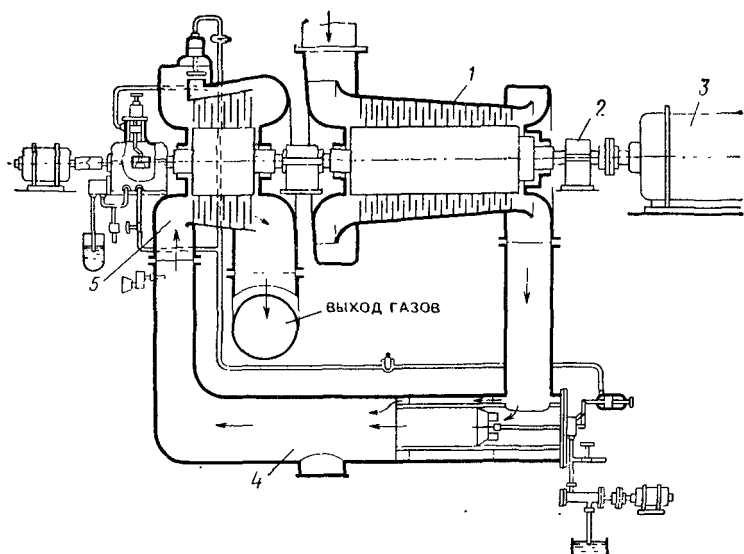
Схема установки осевого компрессора с газовой турбиной
